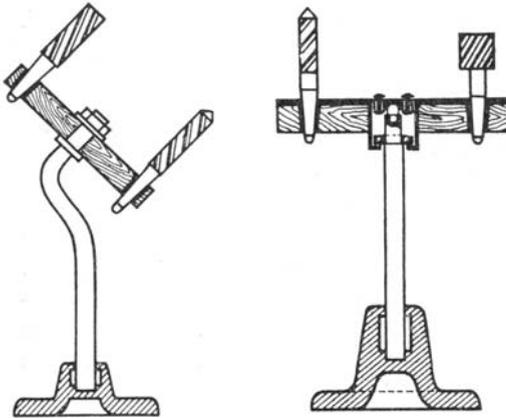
Ständer für Wechselbohrwerkzeuge.
